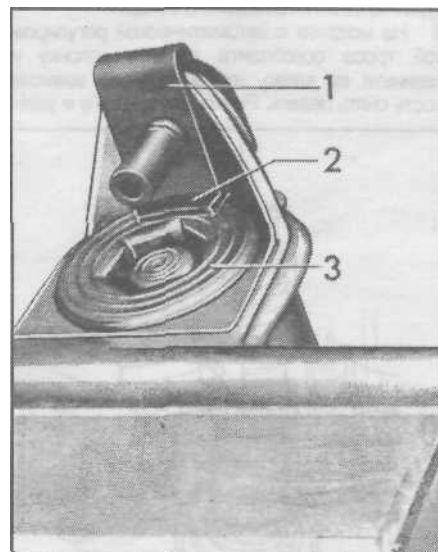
Резиновая направляющая шайба троса сцепления (1) уплотняющая поверхность [2] и торцевая крышка вала выбора передач [3] - коробка передач 020
